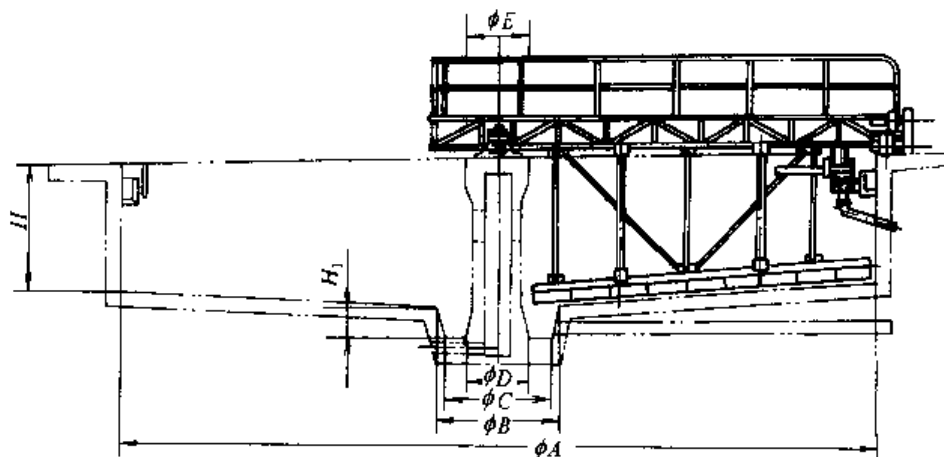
FZNJ 型辐流式周边传动刮泥机外形尺寸
